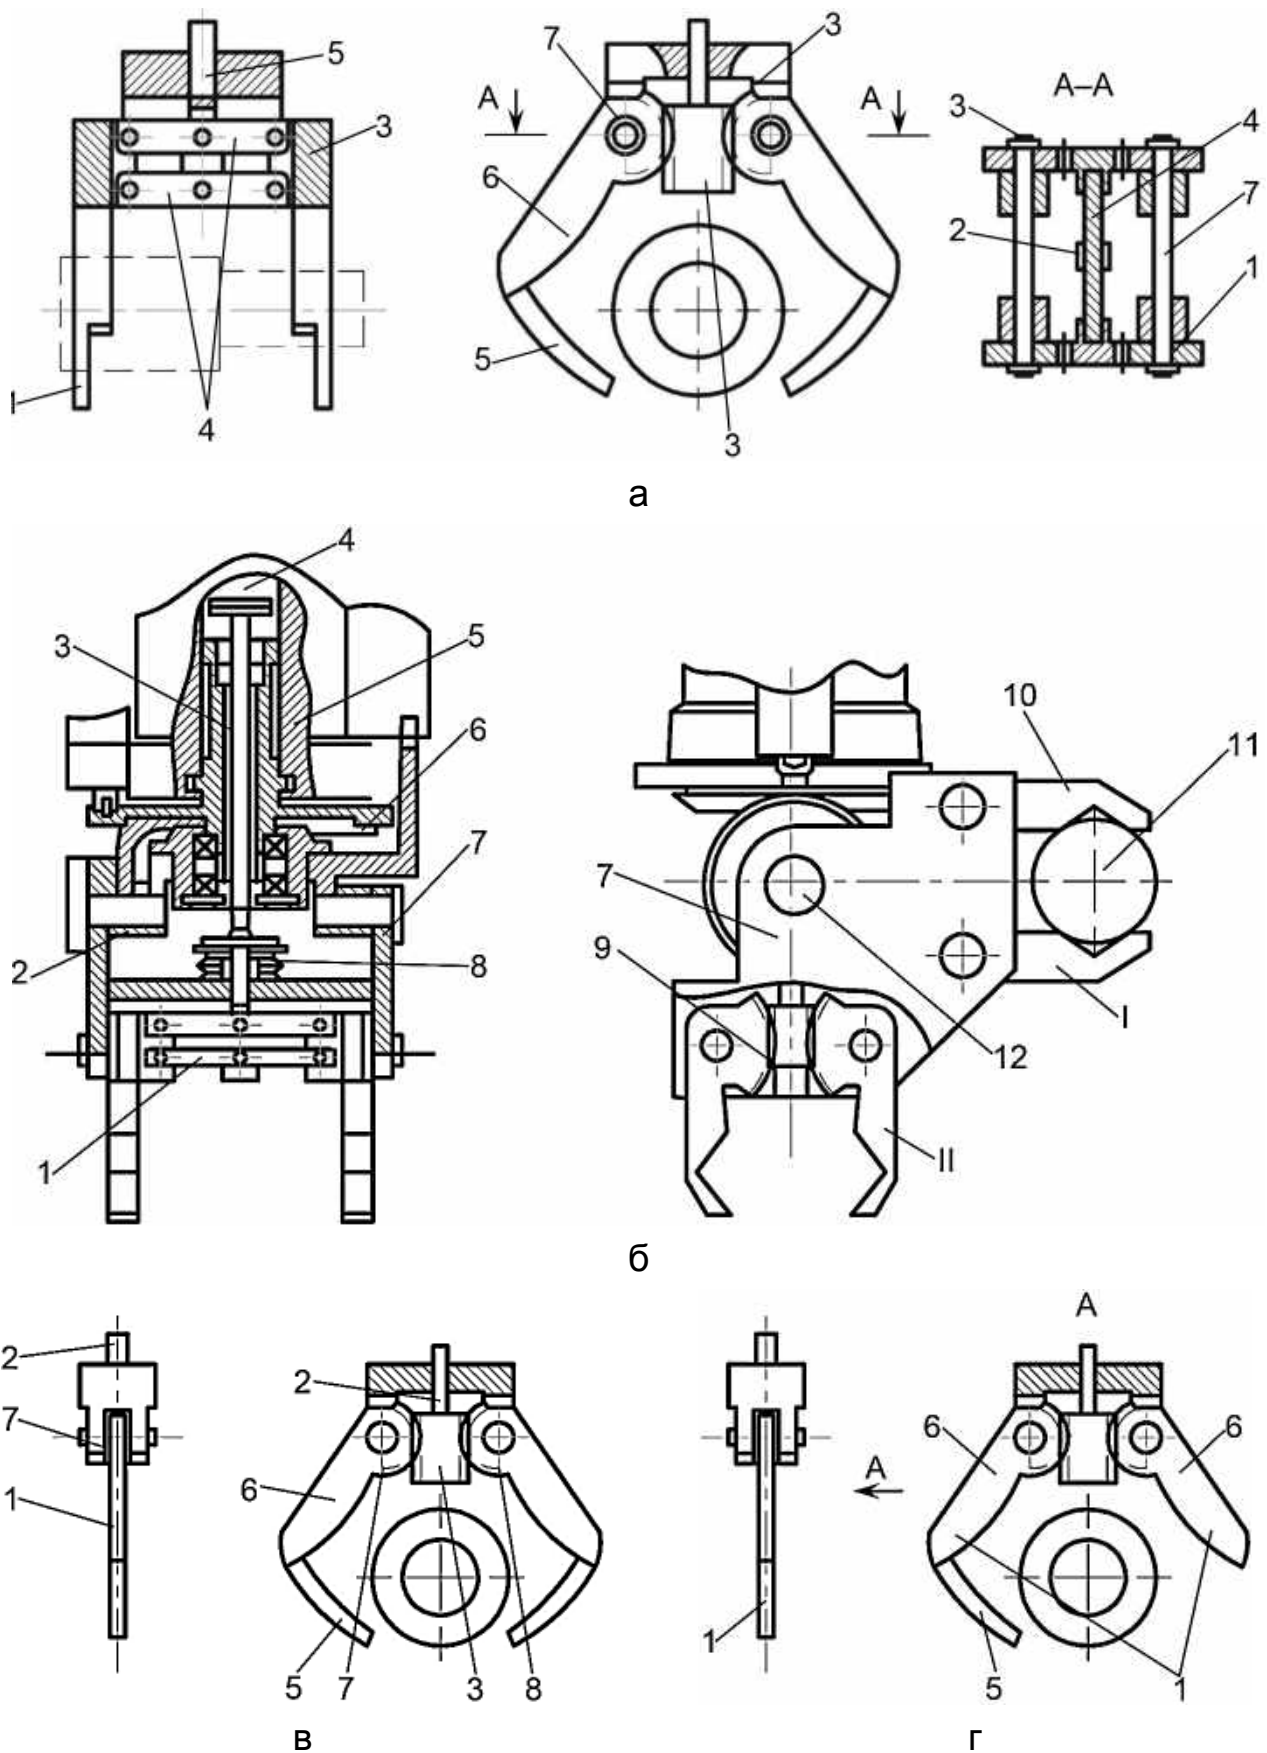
Рейкові широкодіапазонні захоплювальні пристрої для деталей типу тіл обертання
